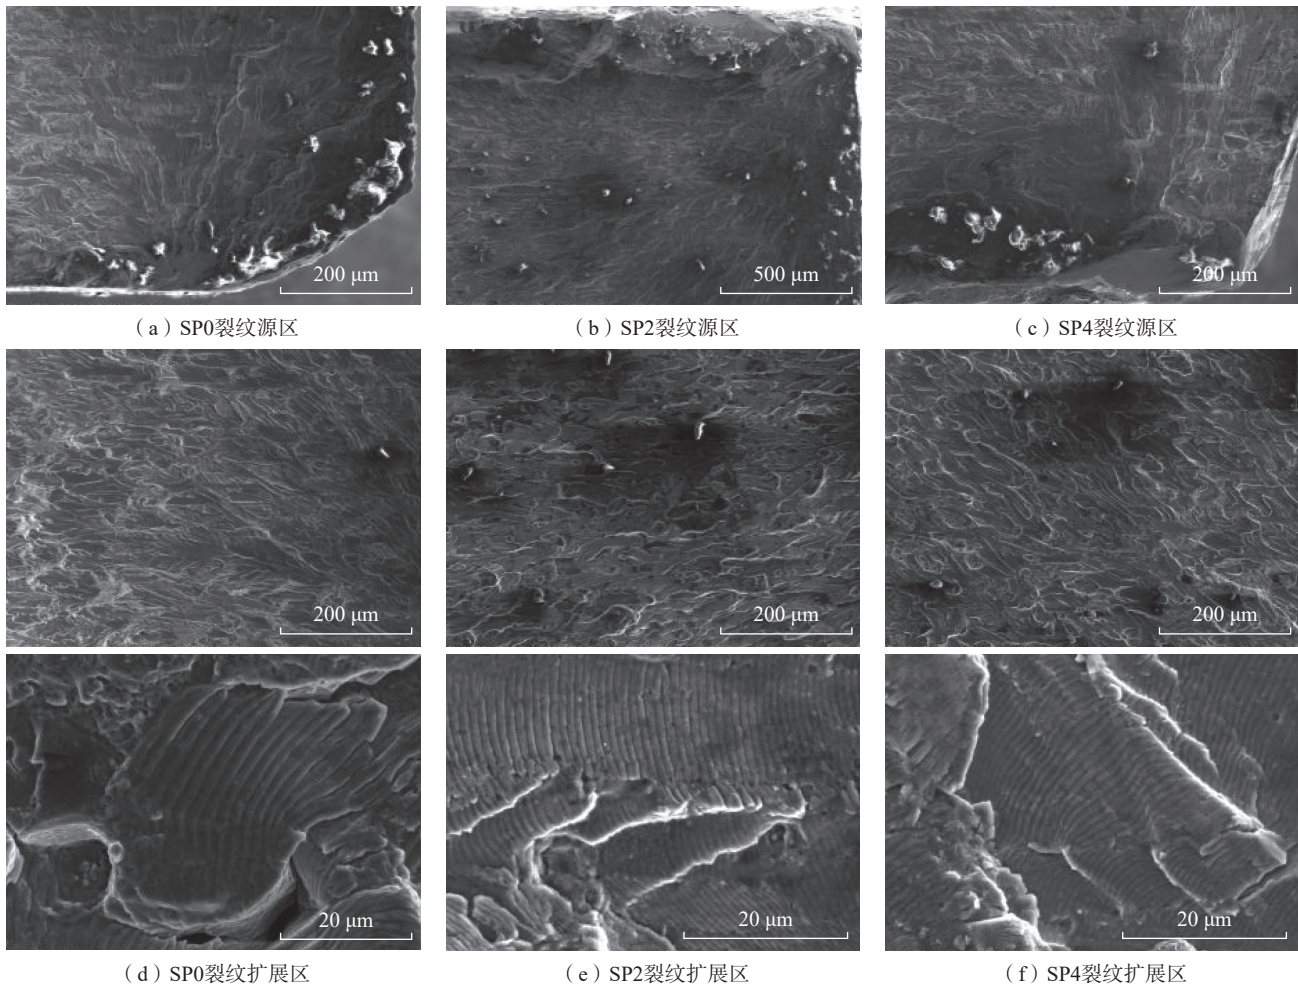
覆铝 7B04-T7451 铝合金试样疲劳断裂断口形貌
